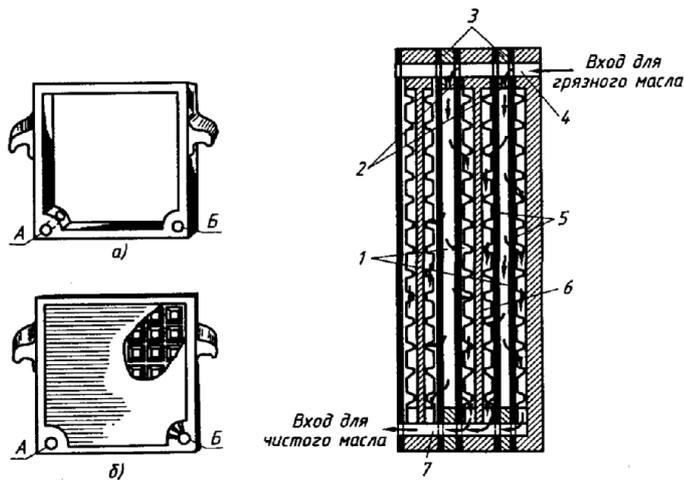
Детали фильтр-пресса (а — рама; б — пластина) и схема его
